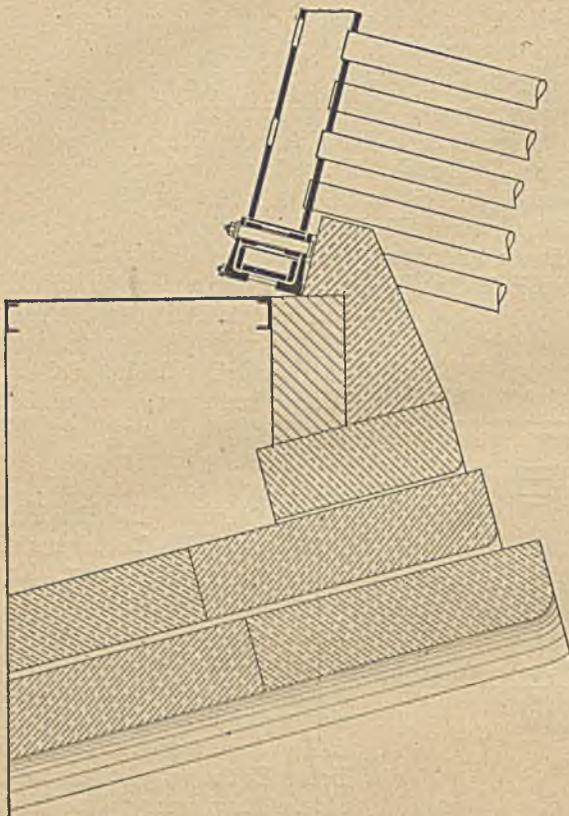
Kammerfreilegung und Sicherung der Schweißnähte nach Münzinger.
